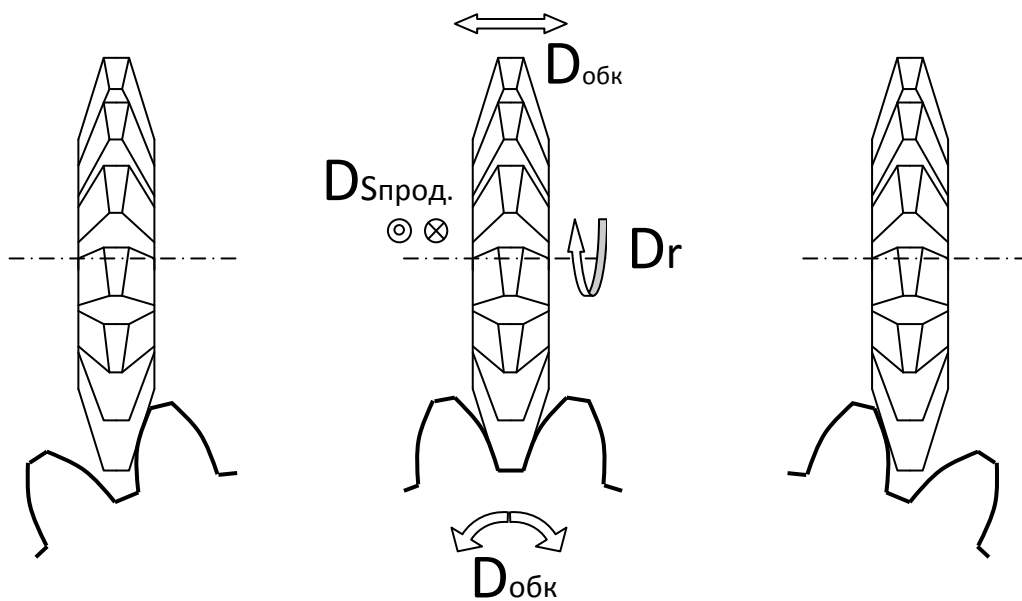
Кинематика формообразующих движений при нарезании прямозубых цилиндрических колес дисковой реечной фрезой
